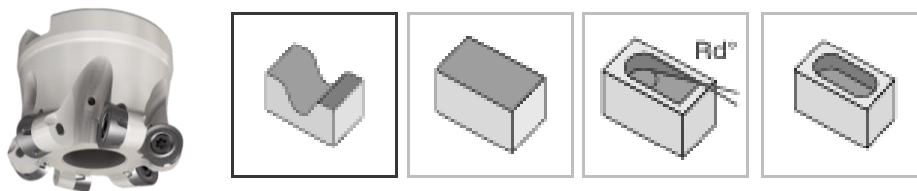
Загальний вигляд і оброблювальні поверхні торцевих фрез типу RoundMill [5]
